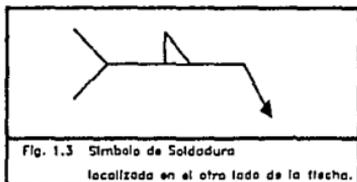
Símbolo de Soldadura localizada en el otro lado de la flecha.
